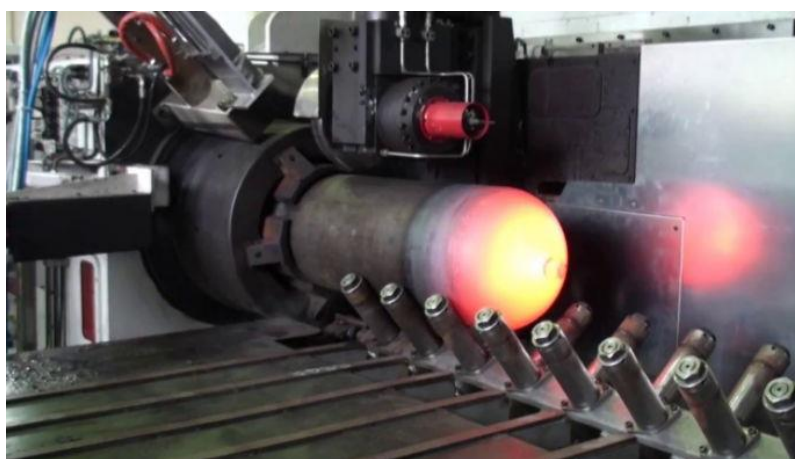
Parrytech Hydraulics_Hydraulic Deep Drawing Press 設備
